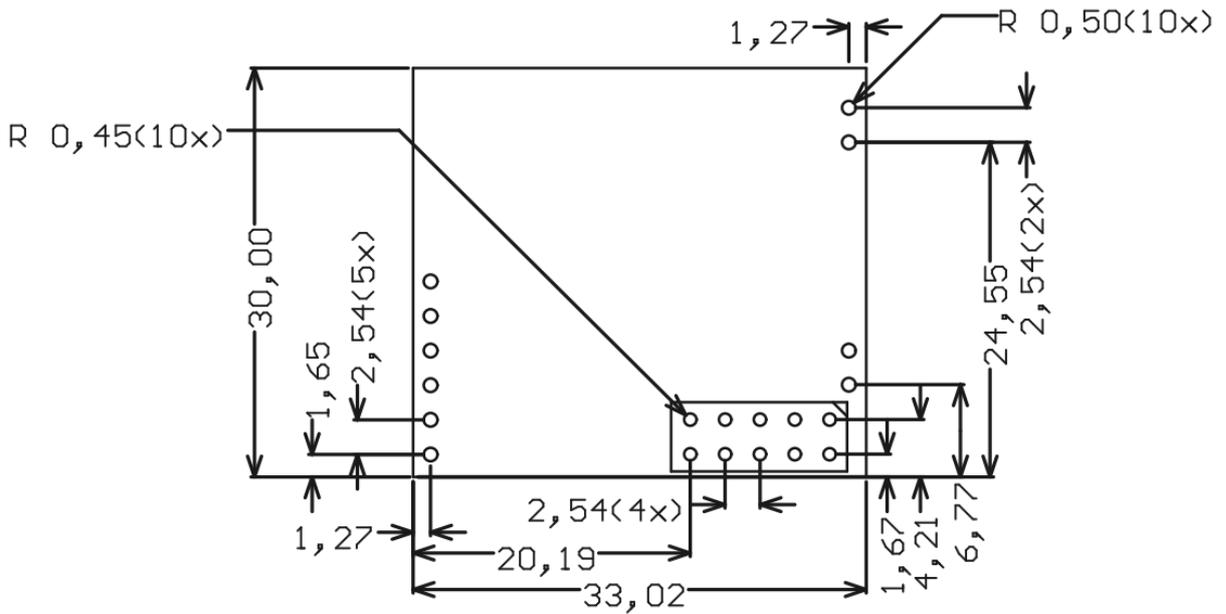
Dimensions et emplacement des broches du MBUS-M13 (en mm)
